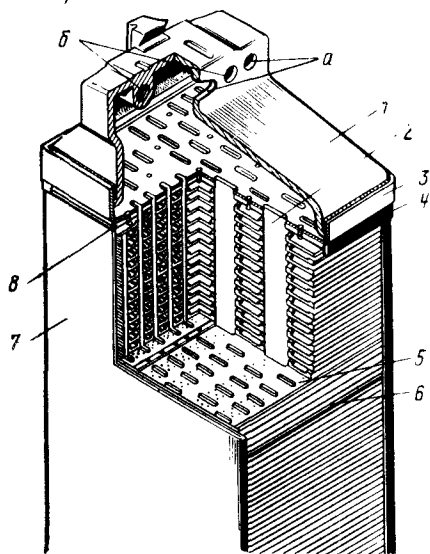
Водовоздушная секция радиатора: 1 — коллектор; 2 — плоская трубка; 3 — трубная коробка; 4 — усилительная пластина; 5 — пластина оребрения; 6 — стяжка; 7 — боковой щиток; 8 — заклепка
